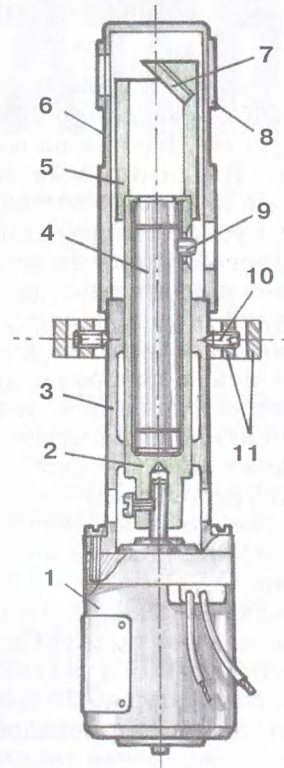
Разрез прибора: 1 — электродвигатель; 2 — вращающийся держатель лазерного генератора; 3 — корпус прибора; 4 — лазерная указка; 5 — насадка отражателя; 6 — колпачок; 7 — зеркало; 8 — шторка обзора; 9 — кнопка включения; 10 — полюсь; 11 — кольца плавающего узла.
